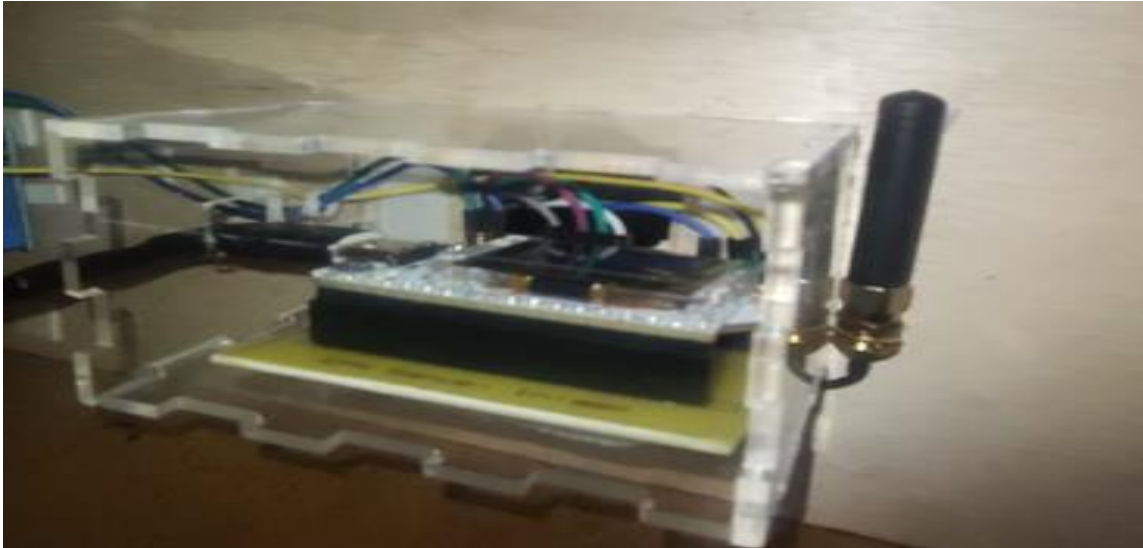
Soldadura de elementos en el PCB
